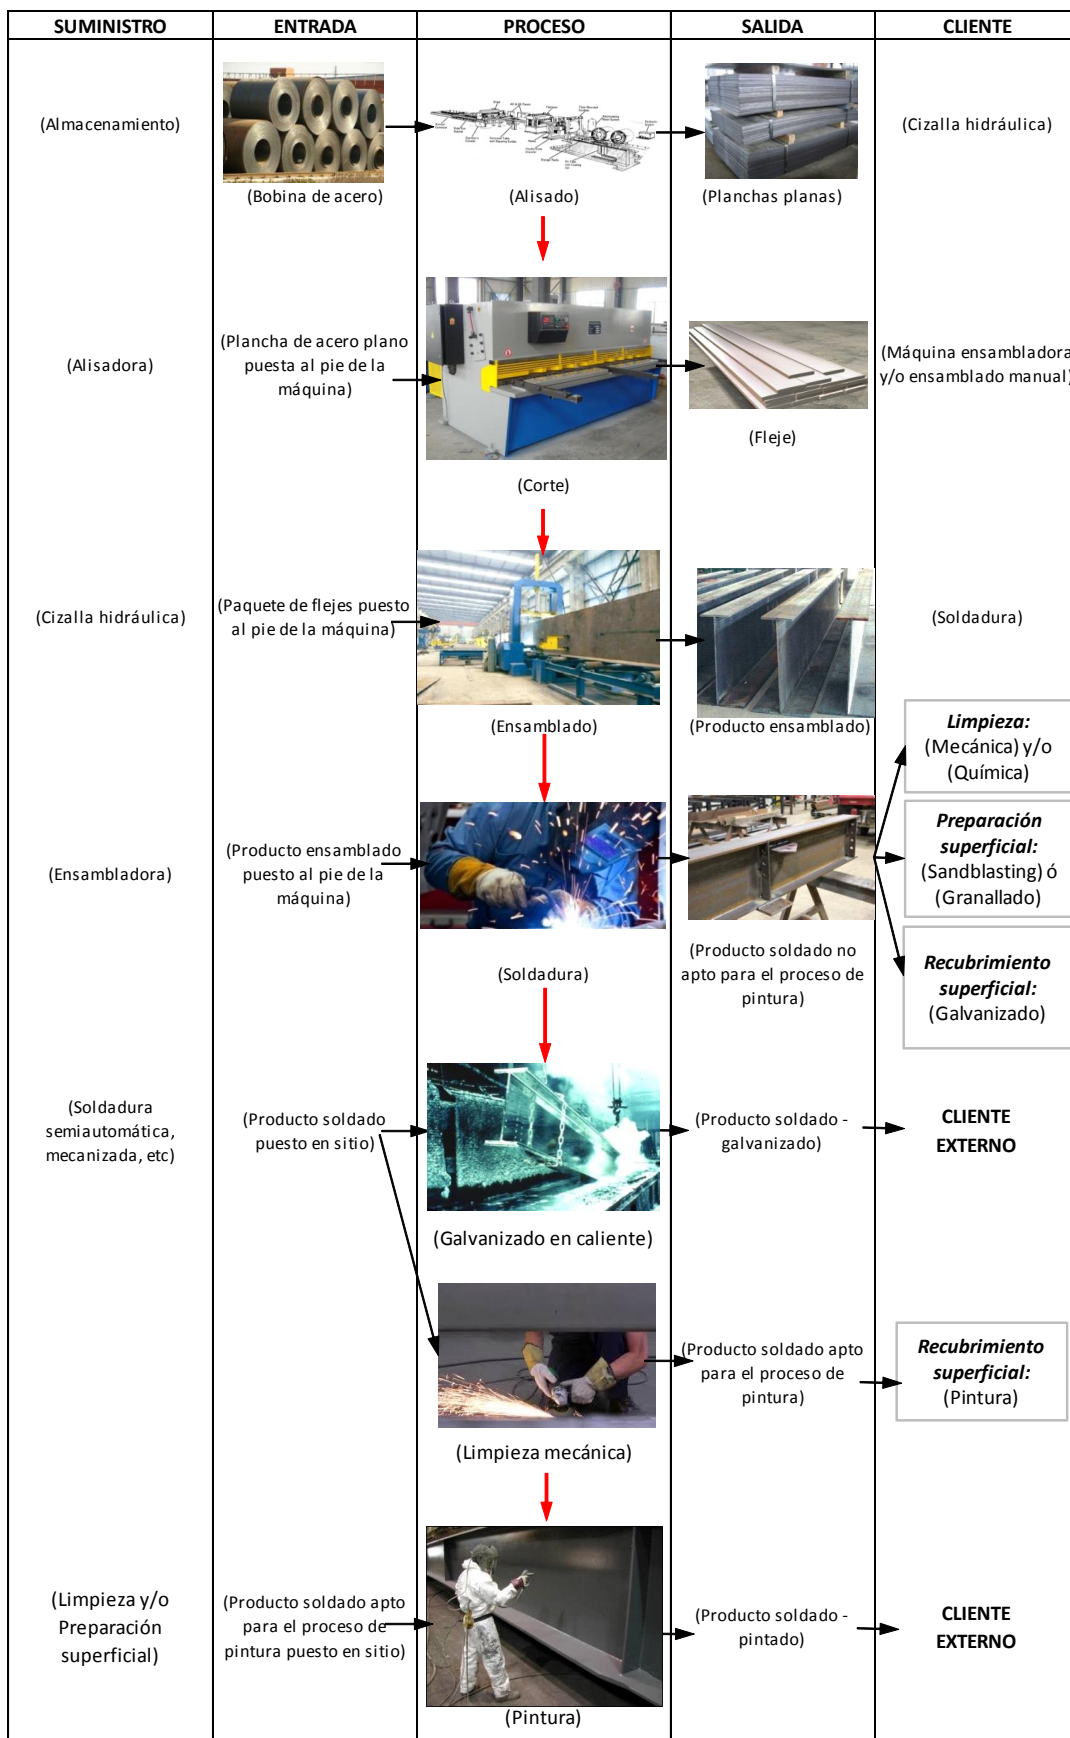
Ruta de Fabricación Típica de un Producto Soldado
